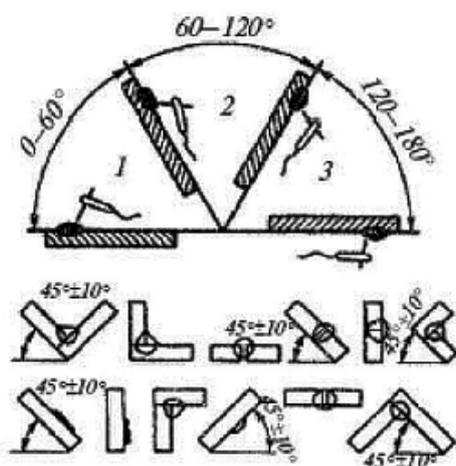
Основные положения сварки и их обозначения:
